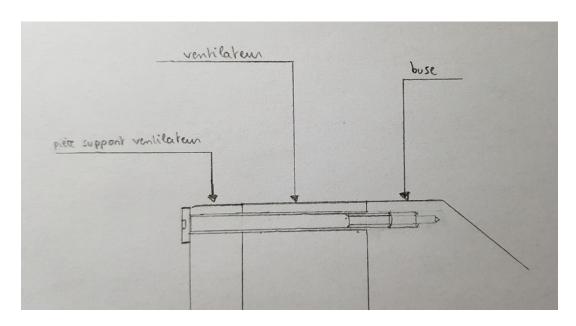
Assemblage support de ventilateur-ventilateur-buse
